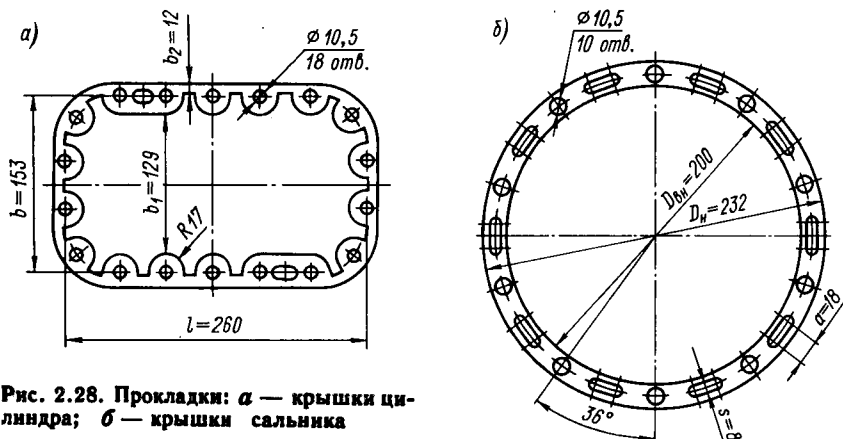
Прокладки: а — крышки цилиндра; б — крышки сальника
